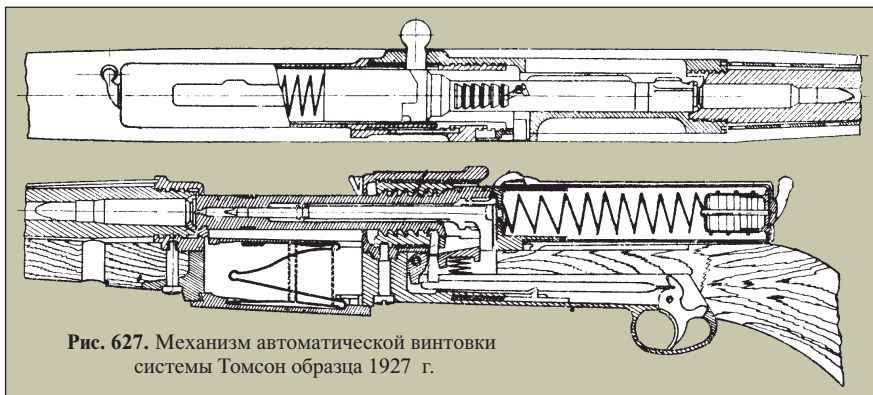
Механизм автоматической винтовки системы Томсон образца 1927 г.
